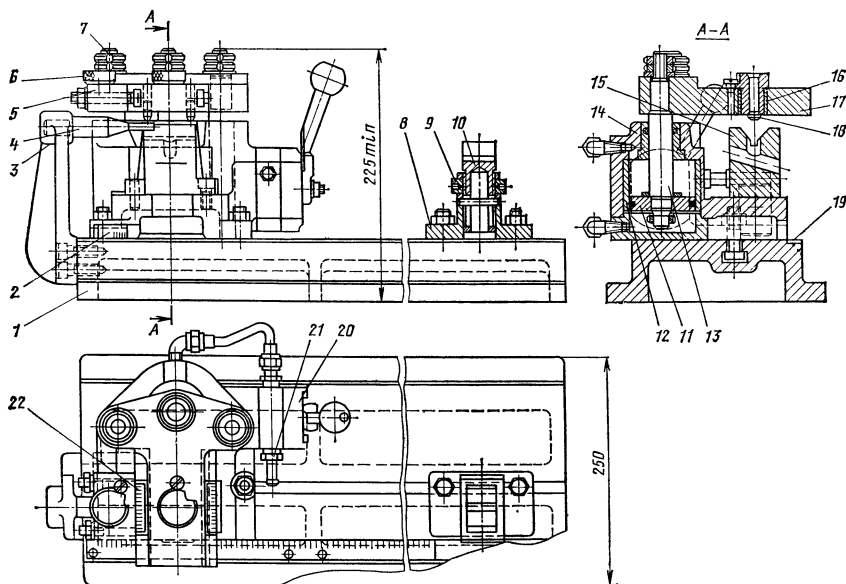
Переналаживаемый скалчатый кондуктор для сверления радиально расположенных отверстий в деталях типа валов
